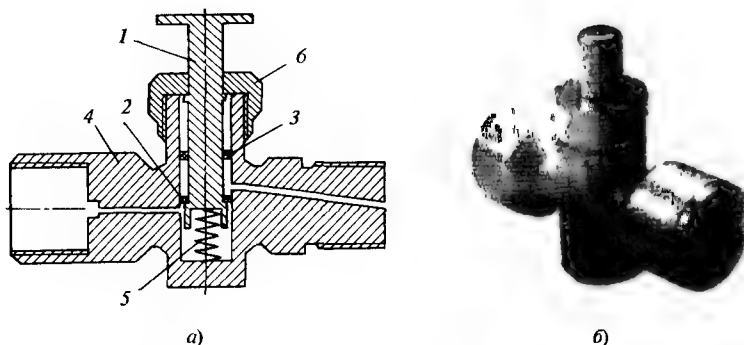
Схема (а) и вид (б) кнопочного включателя манометрического прибора:
